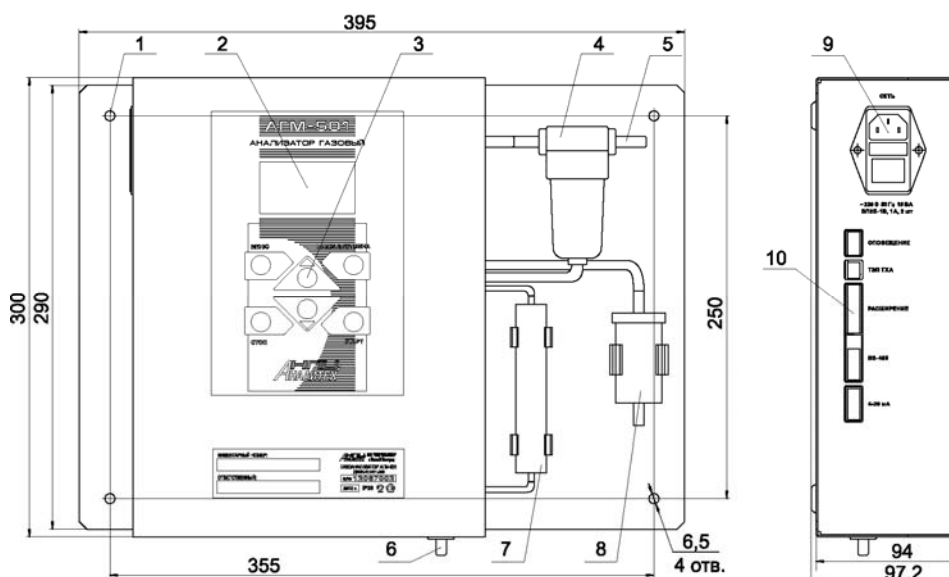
Внешний вид и габаритные размеры газоанализатора АГМ-501
